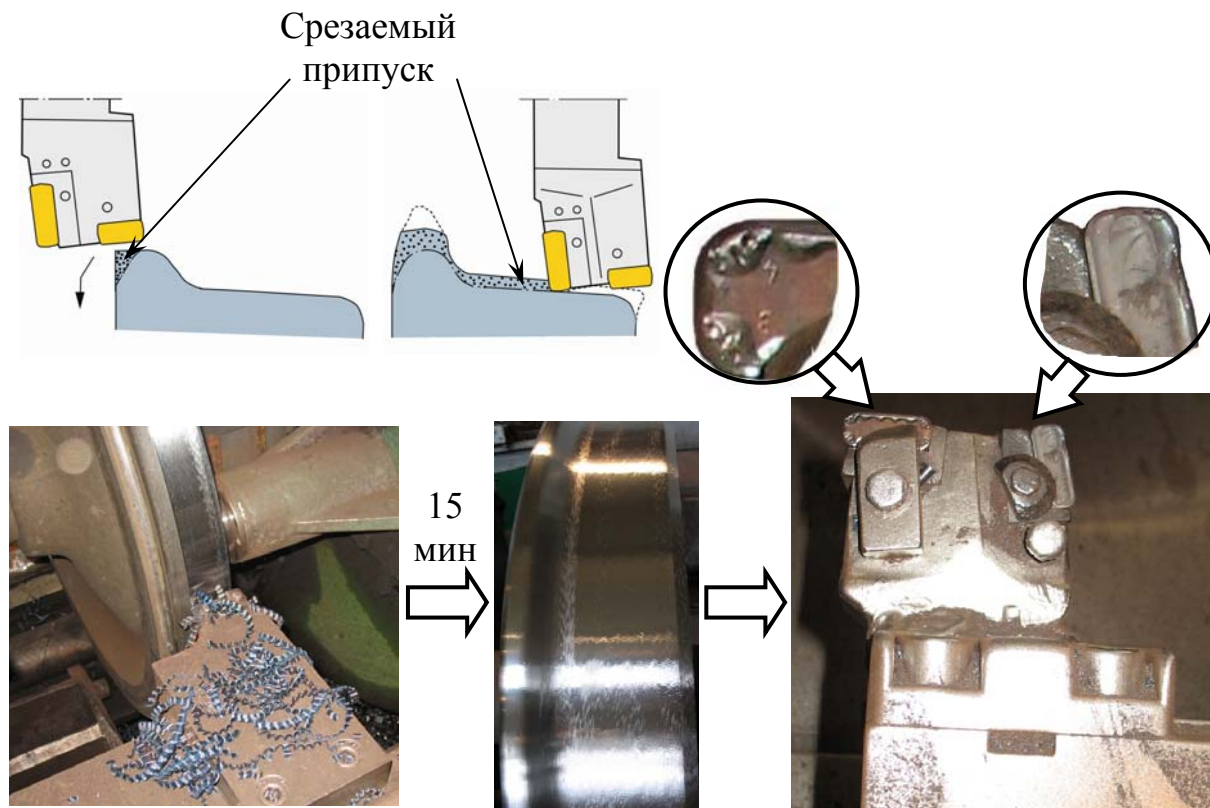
Схема обработки на копировальном колесотокарном станке
